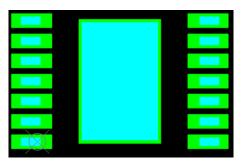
SO-14 PCB パッドの PWP0014L、水色: PWP0014L リード、緑: その他の SO-14 PCB パッド
